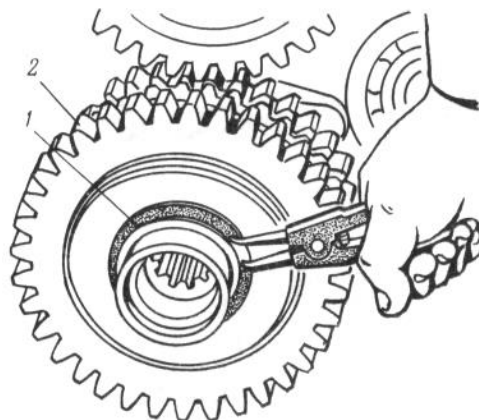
Знімання стопорного кільця проміжної шестерні понижуючого редуктора: 1- стопорне кільце; 2- проміжна шестерня.
